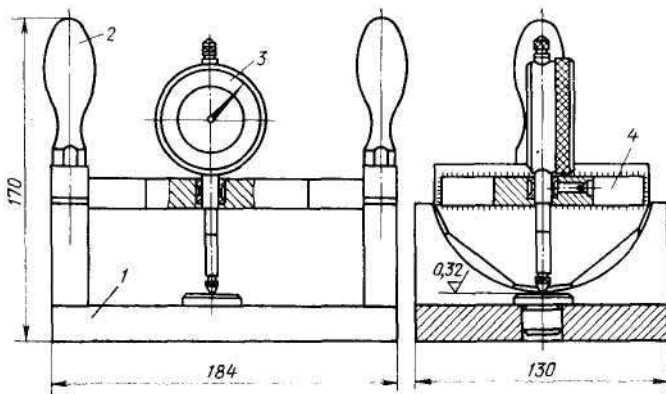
Контрольное приспособление для подбора толщины регулировочных шайб:
